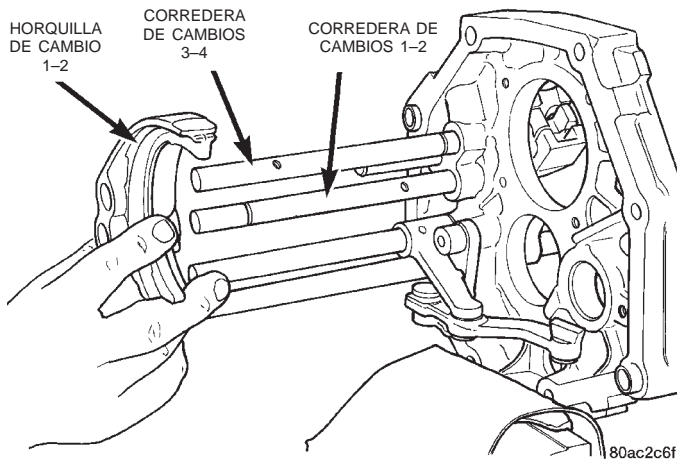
Desmontaje de la horquilla de cambio 1-2
